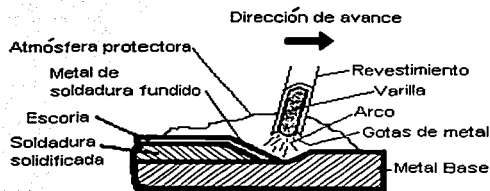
Características del proceso de soldadura SMAW.
